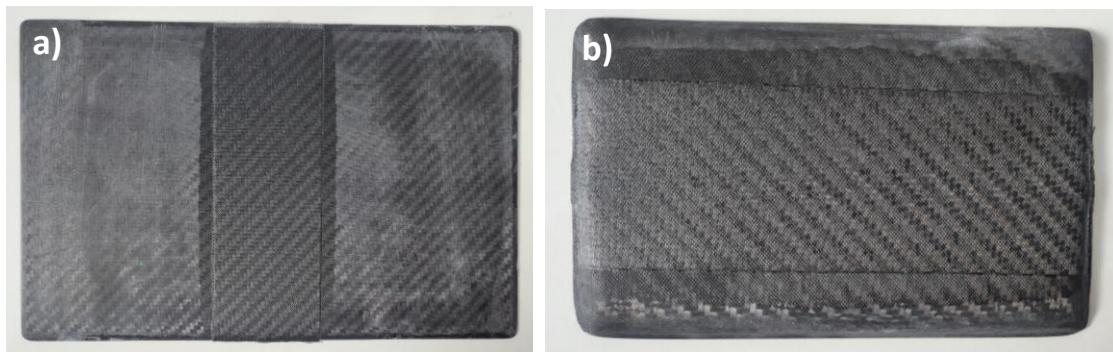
Processo de reparação por preenchimento da fissura: a) placa reparada para ensaios à tração; b) placa reparada para ensaios à flexão
